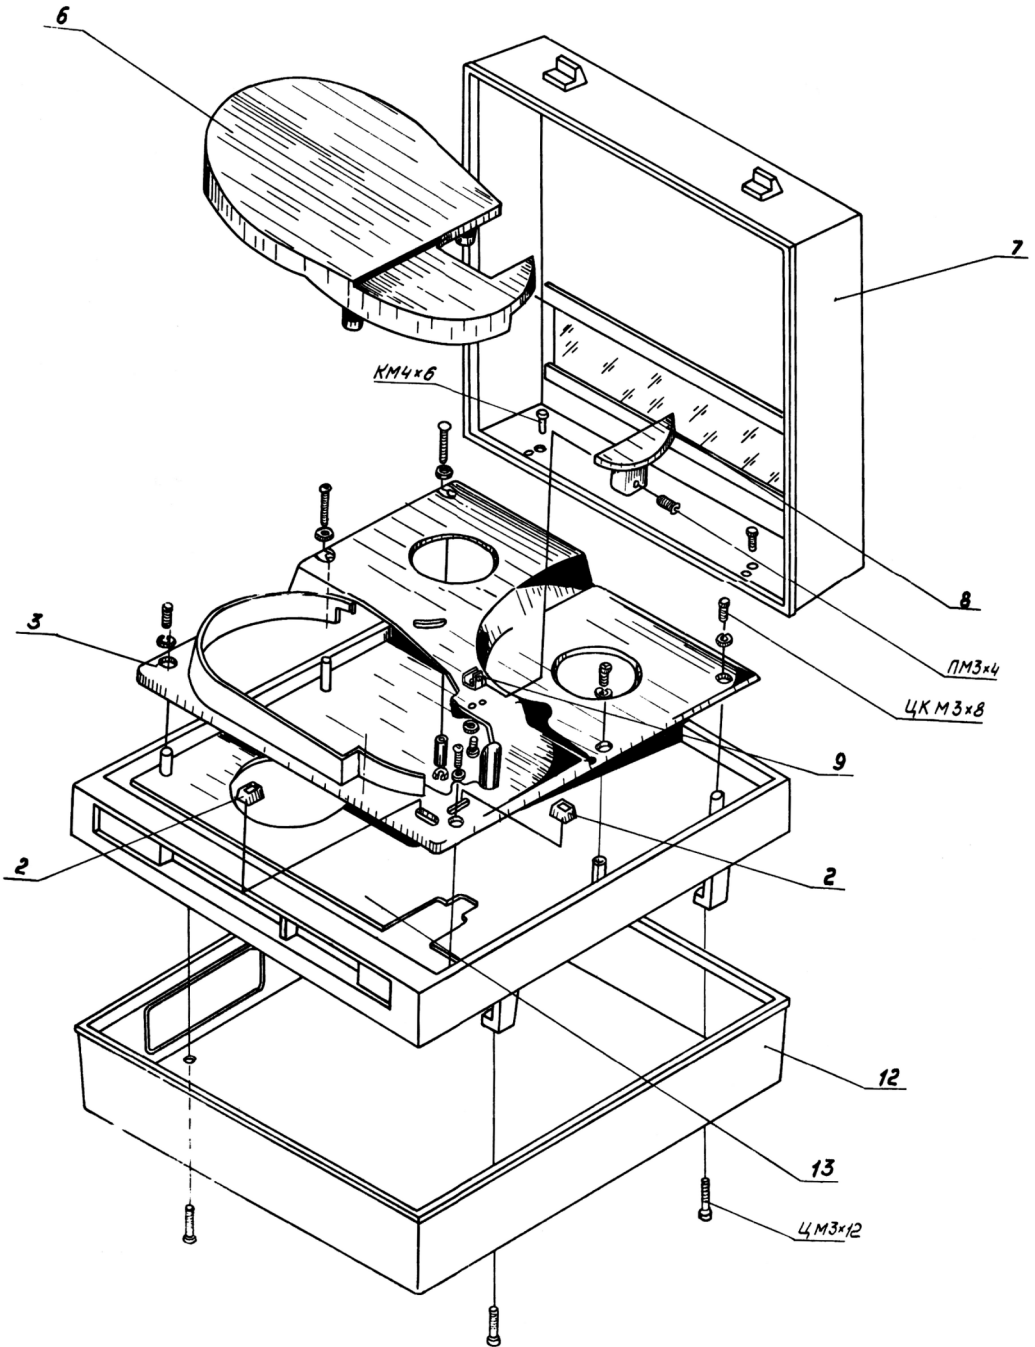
Схема разборки (сборки) корпуса видеоманитрона
